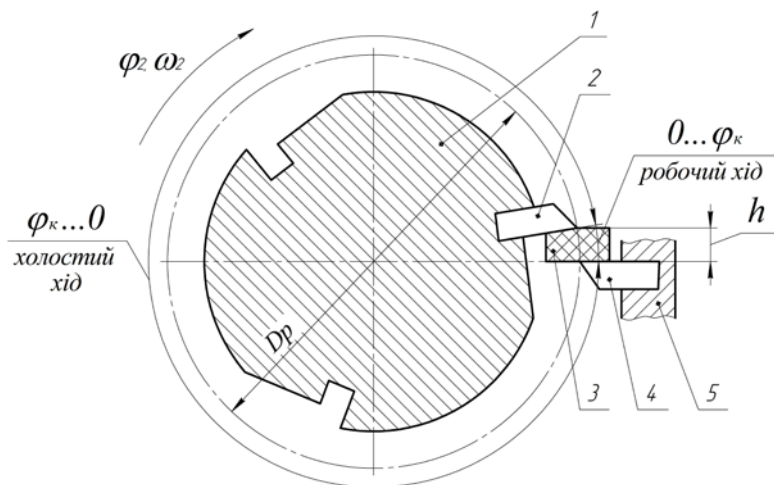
Розрахункова схема взаємодії робочого органу роторної ножової дробарки та матеріалу що переробляється: 1 – ротор; 2 – рухомий ніж ротора; 3 – матеріал, що переробляється; 4 – нерухомий ніж корпусу; 5 – корпус
